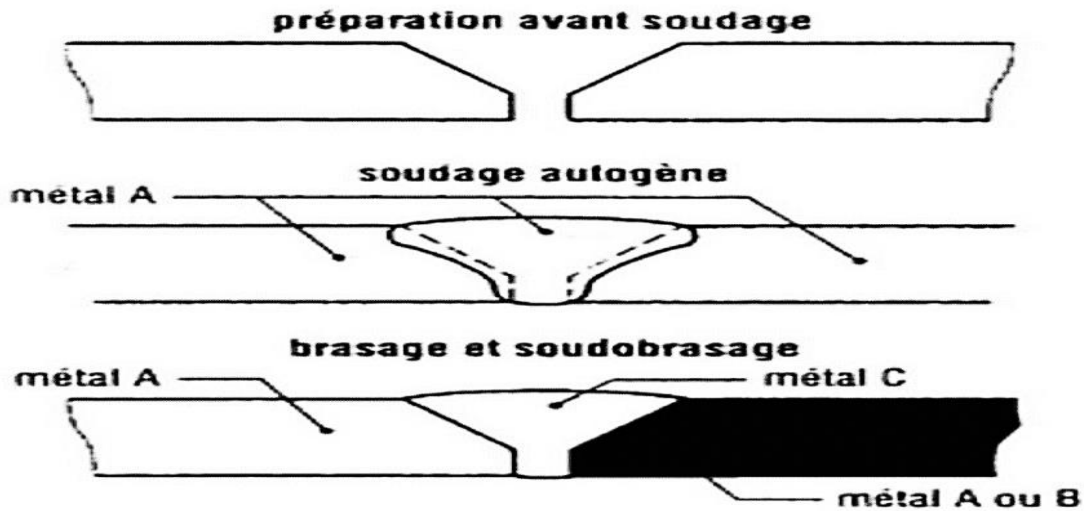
Assemblage de deux pièces par soudage [20].
